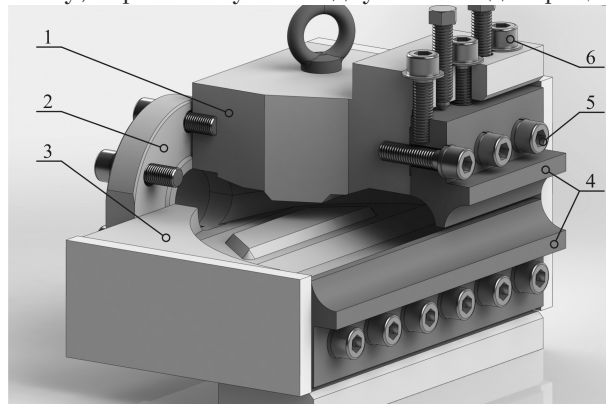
Ескіз плоскощільової головки для формування плит з XPS: 1 – верхня плита; 2 – адаптер; 3 – нижня плита; 4 – губки; 5 – прижимні гвинти; 6 – регулюючі гвинти.
